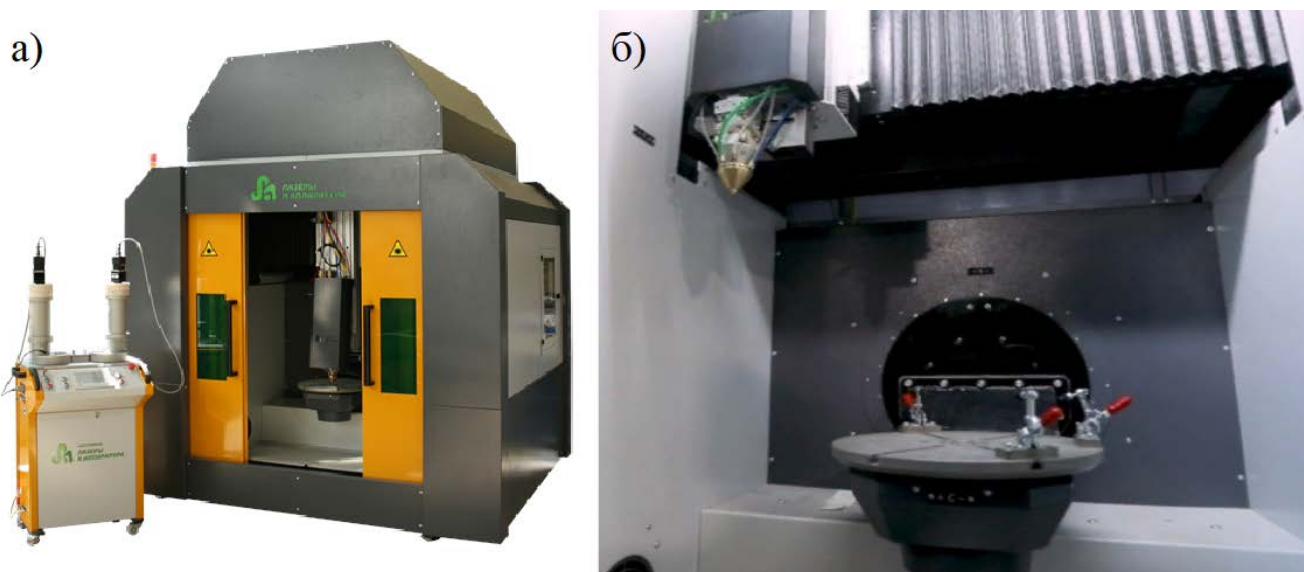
Внешний вид установки лазерной наплавки МЛ7 (а), рабочая камера построения (б)
